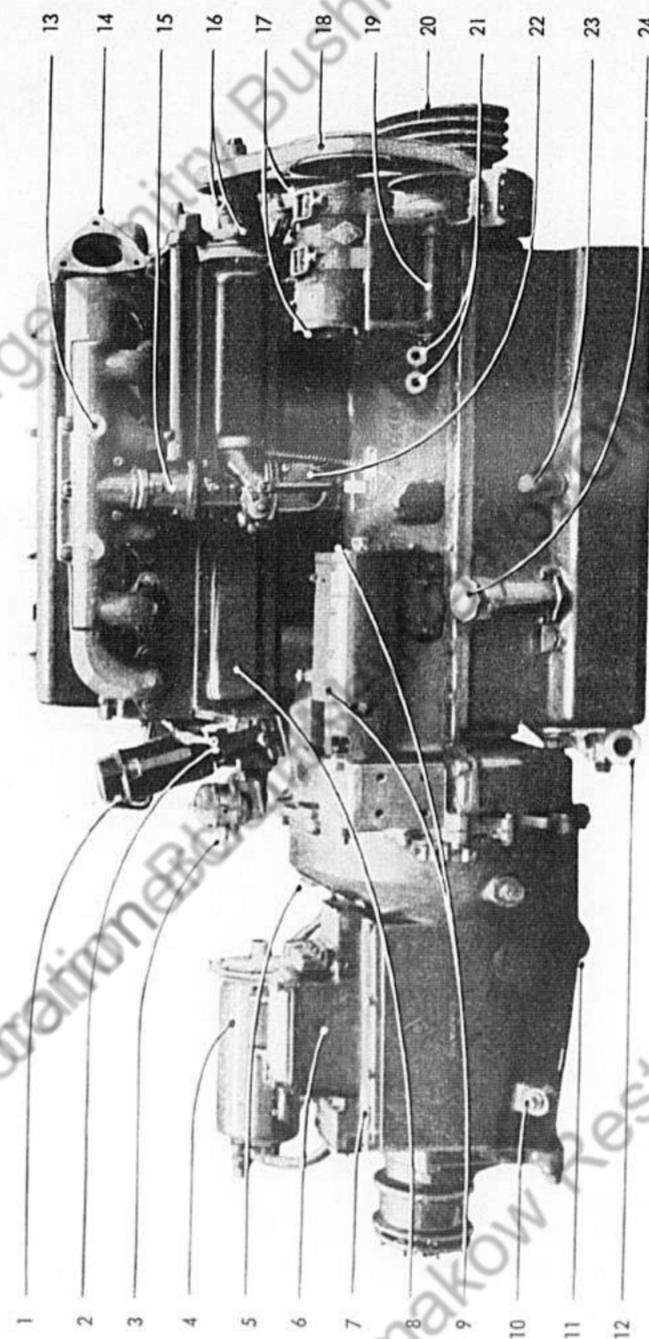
Außenansicht des Motors (Schwanzflanken-Anlasserseite) mit Hauptkupplung und Schaltgetriebe
